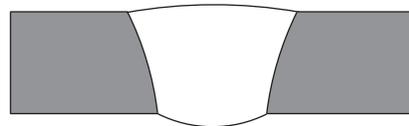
Exemple de soudure incorrecte n° 8
